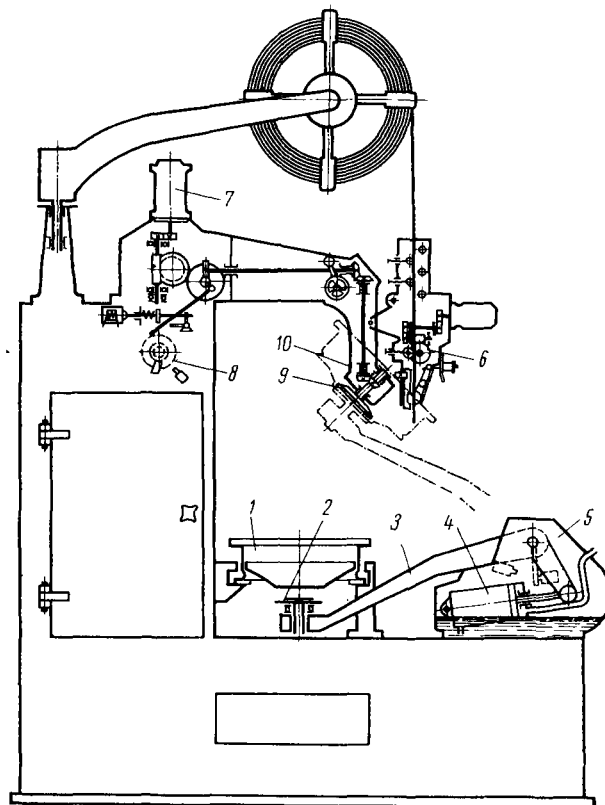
Схема автомата для электродуговой сварки колес
